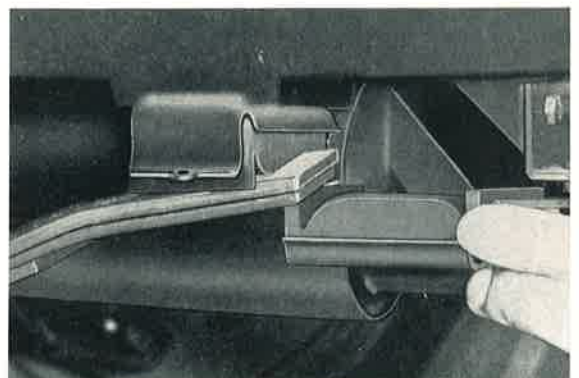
/4: Die Auflage wird zur Seite gedreht und die Feder aus dem Gummiblock-Lager herausgenommen.
